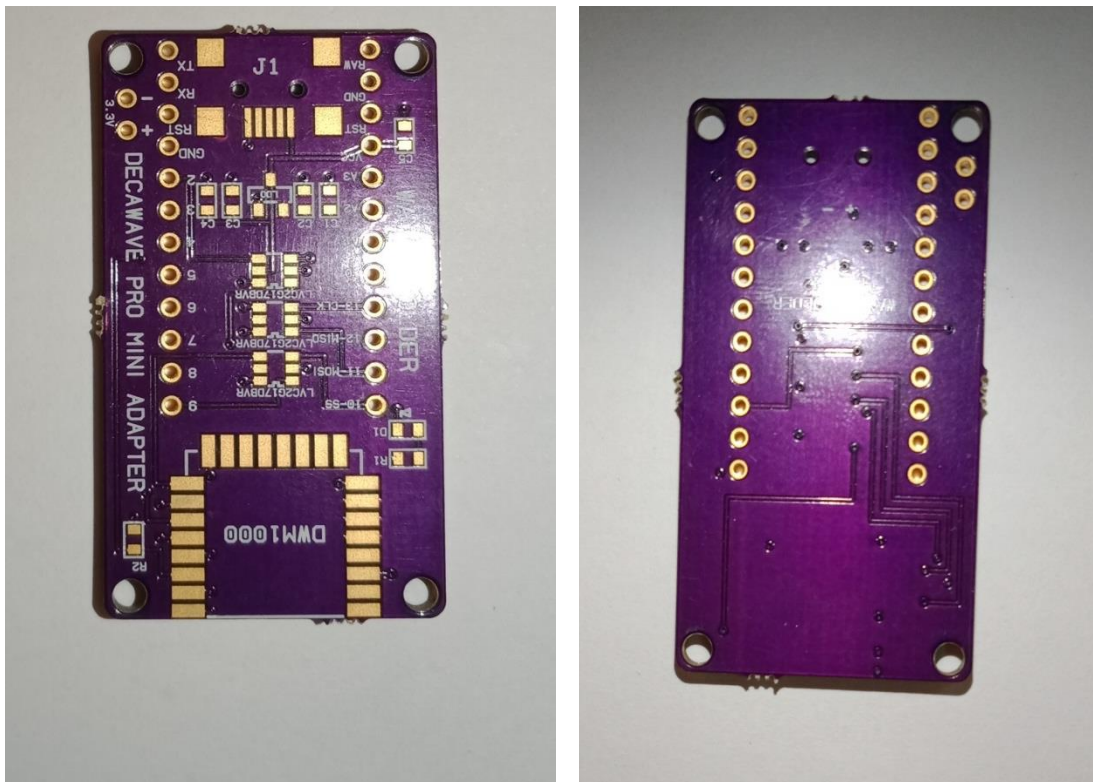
Disposition du circuit imprimé (Haut et bas)
